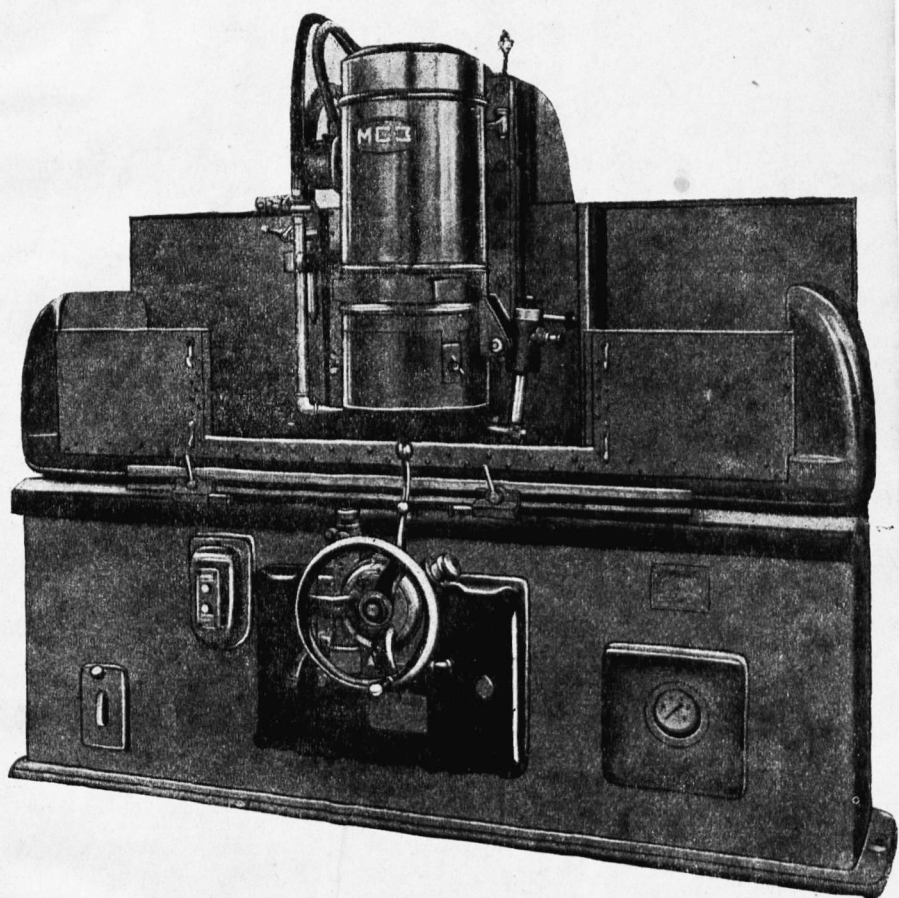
Общий вид плоскошлифовального станка с вертикальным шпинделем Московского станкостроительного завода (МСЗ), тип 3732
